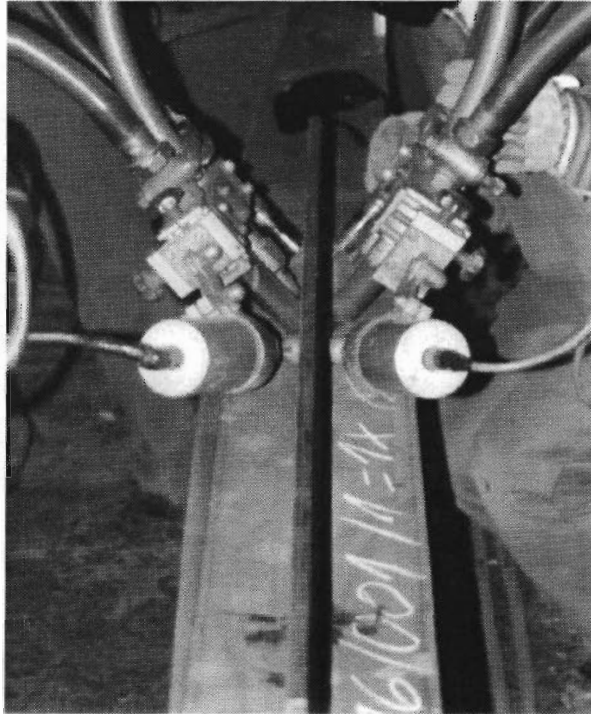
MAG-Schweißen der Rohlinge mittels Automaten
